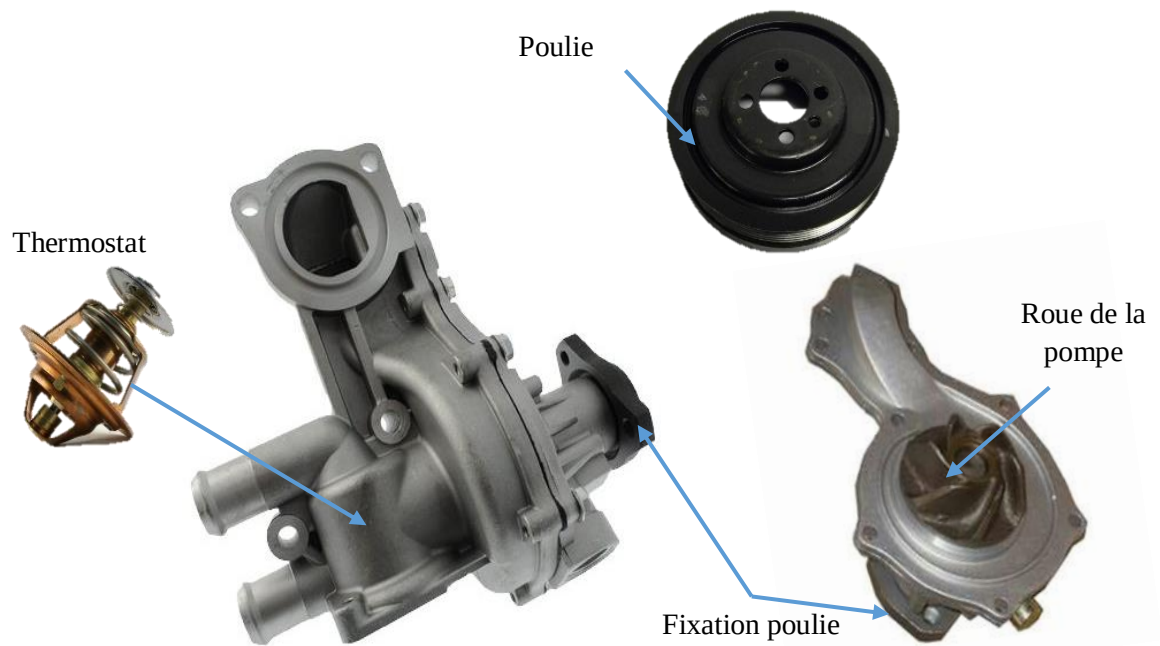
Vue éclatée de la pompe à eau VW D1600.
